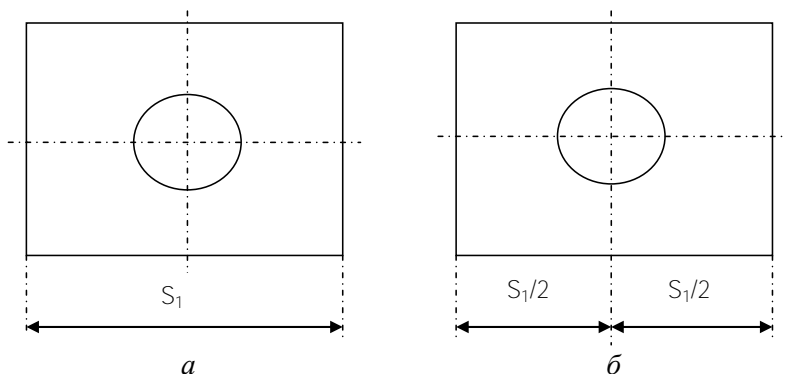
Размеры на чертеже детали (а) и схеме обработки (б)
